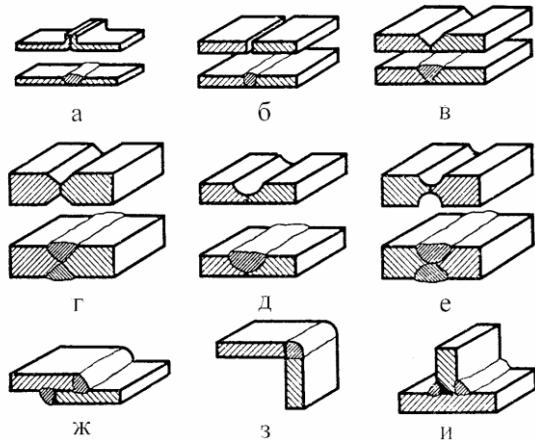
Виды сварных соединений и способы разделки кромок:
